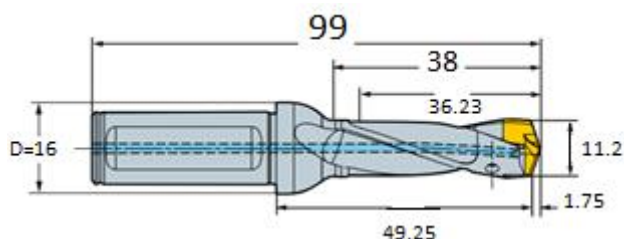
Сверло CoroDrill®870 870-1100-8L16-3
